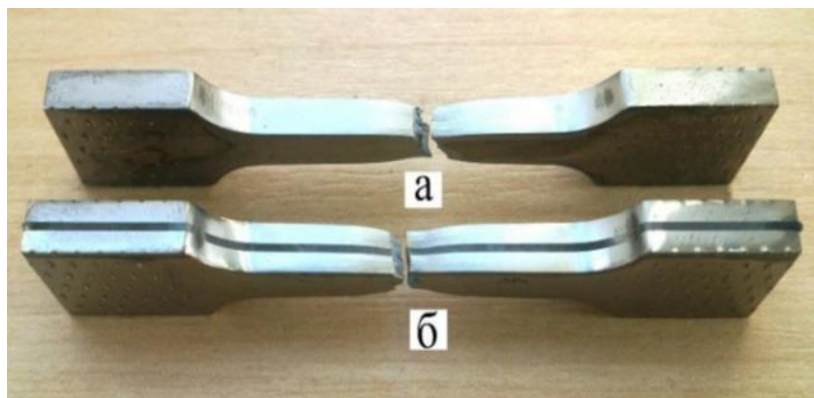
Внешний вид разрушенных сварных образцов, после испытания на растяжение: а) сварка без промежуточного листа и б) сварка через промежуточный сверхпластичный лист [17].
